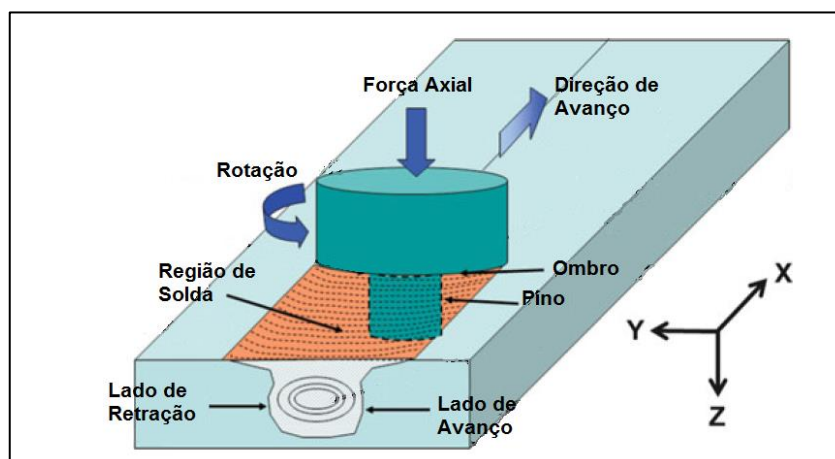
Desenho esquemático do processo de *Friction Stir Welding* (MISHRA; KUMAR, 2014).
